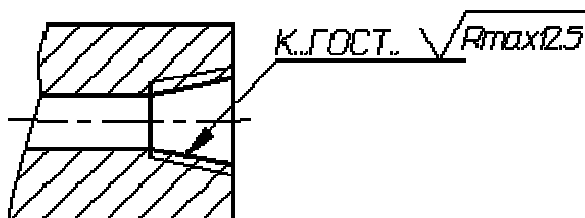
Пример обозначения шероховатости внутренней конической резьбы
